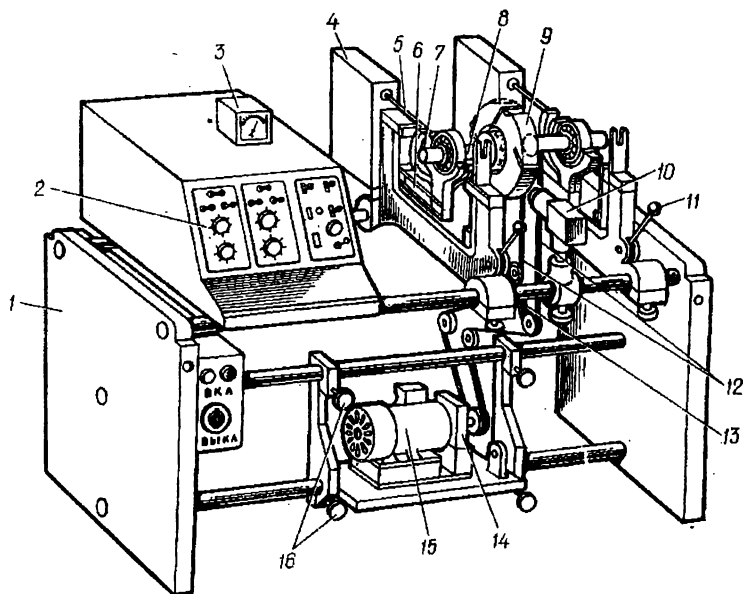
Станок для динамической балансировки ДБ-10:
